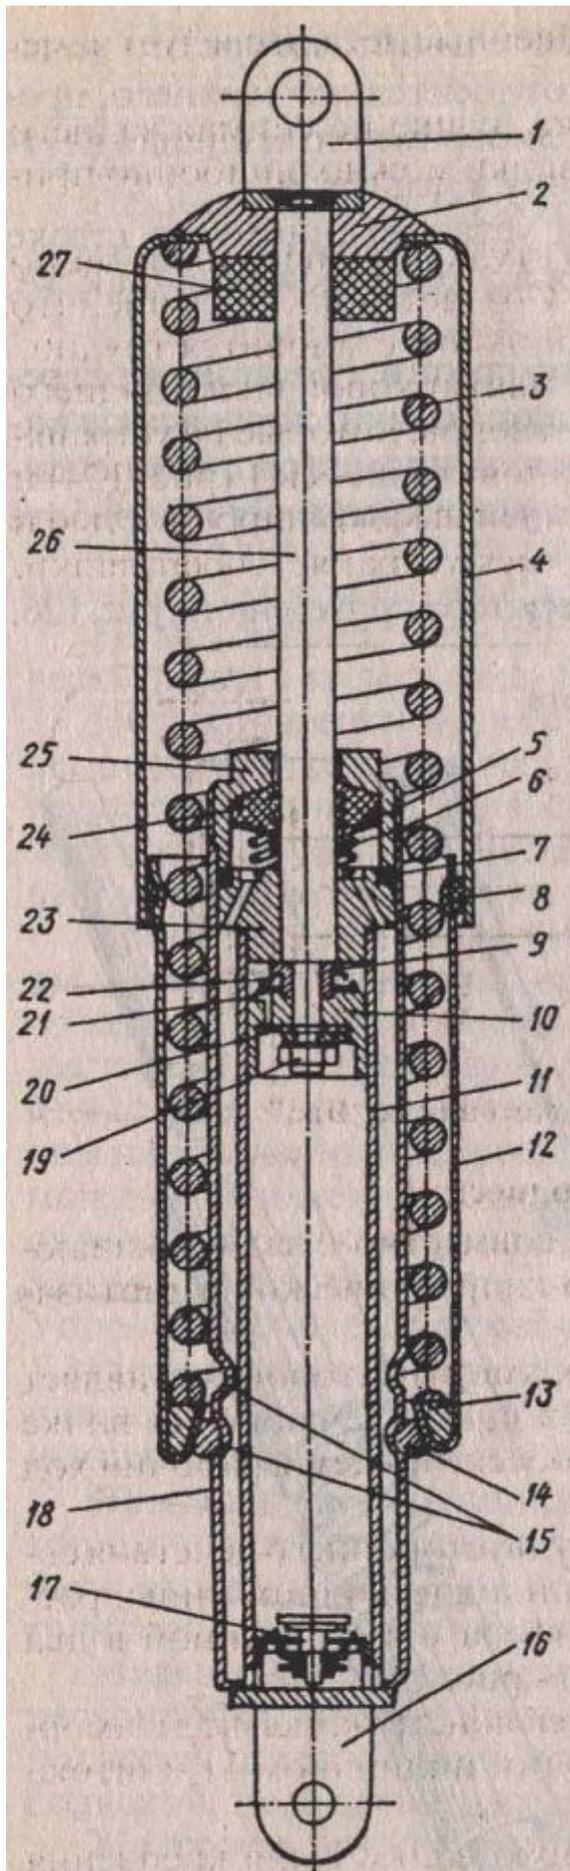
Разрез пружинно-гидравлического амортизатора задней подвески: 1 - вилка штока; 2 - упор верхнего кожуха; 3 - пружина; 4 - верхний кожух; 5 - шайба сальника; 6 - пружина лабиринтного сальника; 7 - резиновое уплотнение; 8 - пластиковое кольцо; 9 - распорная втулка; 10 - поршень; 11 - рабочий цилиндр гидравлического демпфера; 12 - нижний кожух; 13 - упорное кольцо пружины; 14 - сухарь; 15 - установочные канавки в корпусе; 16 - вилка корпуса; 17 - нижний клапан цилиндра; 18 - корпус гидравлического амортизатора; 19 - гайка поршня; 20 - нижний клапан; 21 - верхний клапан; 22 - пружина верхнего клапана; 23 - направляющая втулка штока; 24 - лабиринтный сальник; 25 - гайка сальника; 26 - шток; 27 - резиновый буфер
